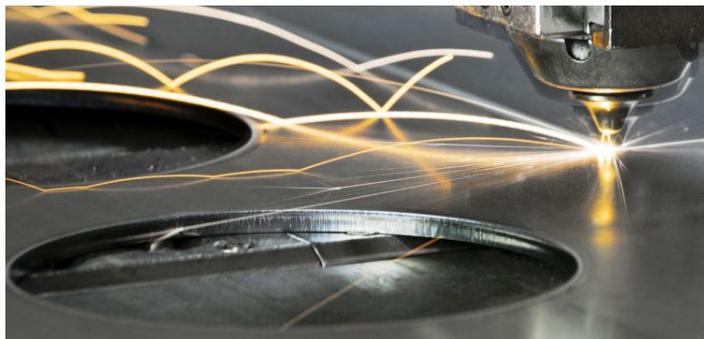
corte a laser, fonte - [www.lasindustria.pt](http://www.lasindustria.pt)
